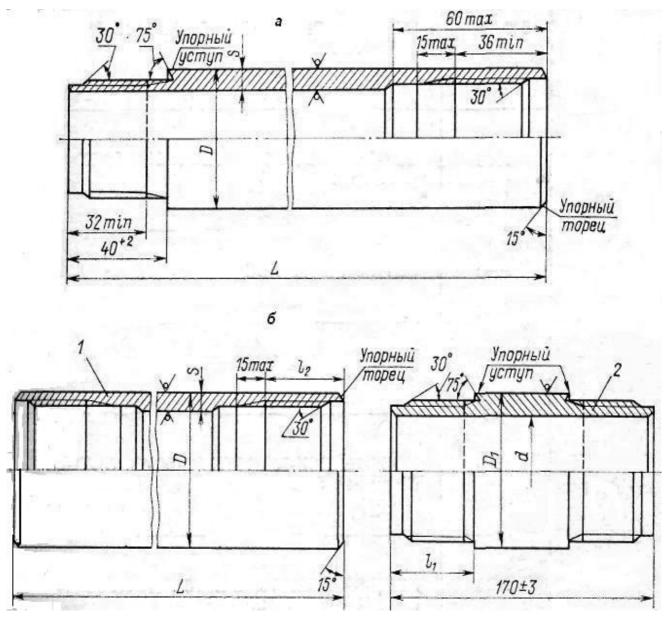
Соединения колонковых труб: а- труба в трубу; б - ниппельные
